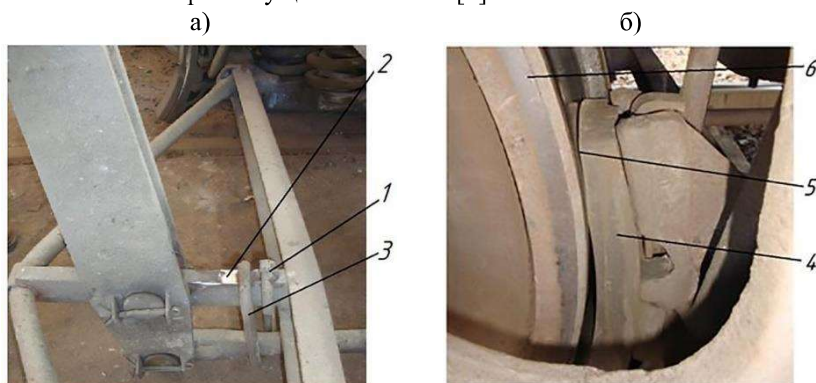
Характерний вигляд в умовах експлуатації: а) – пошкодженого типового пристрою рівномірного зносу колодок; б) – схиленої та притиснутої верхівки гальмової колодки до поверхні кочення колеса; 1 – зруйнований замок; 2 – стертість розпірки триангеля; 3 – петля; 4 – гальмова колодка; 5 – стертість верхівки колодки; 6 – колесо
